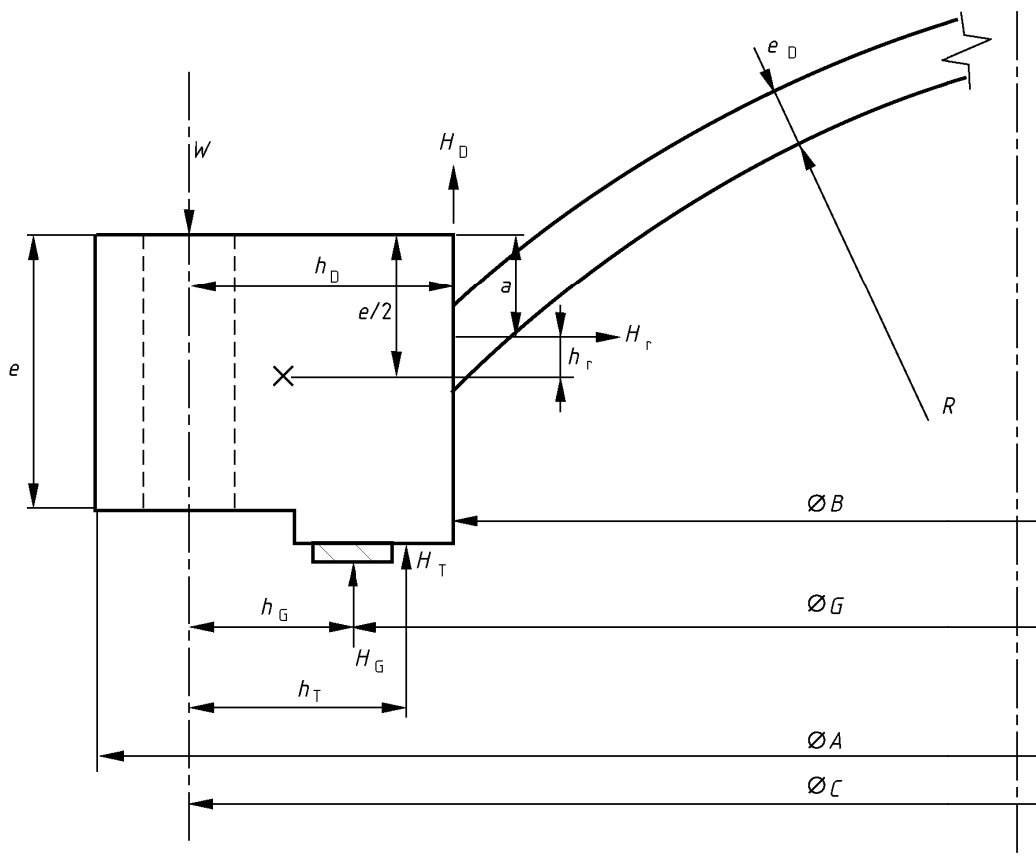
Fondo de cúpula atornillado con junta de cara estrecha
